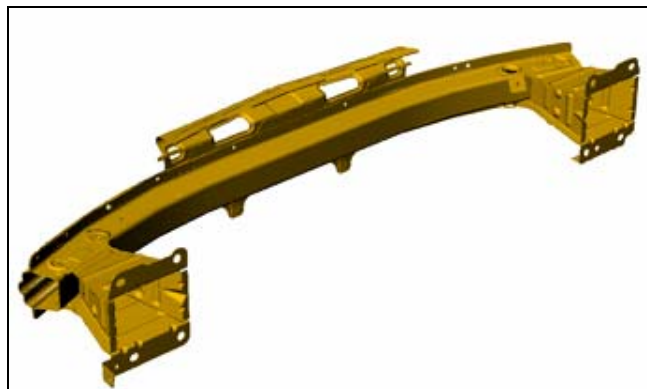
Conjuntos de peças soldadas e montadas.
